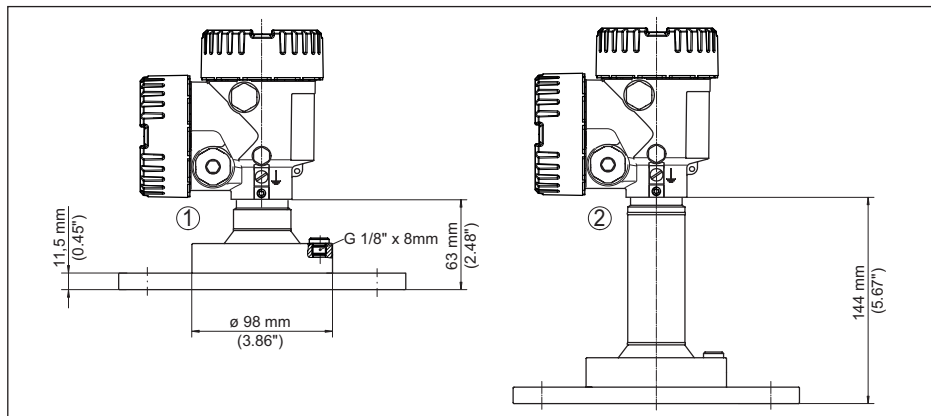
NCR-86, flange com antena lentiforme (espessura do flange, vide desenho, tamanho do flange conforme DIN, ASME, JIS)
